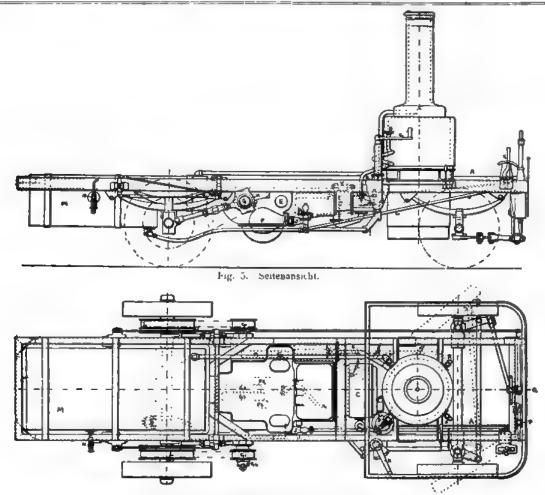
Grundriss des Coultbard'schen Dampf-Lastwagens.
